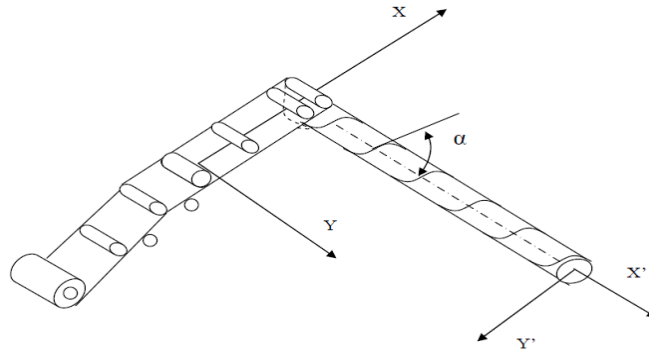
Principe de fabrication d'un tube soudé en spirale
